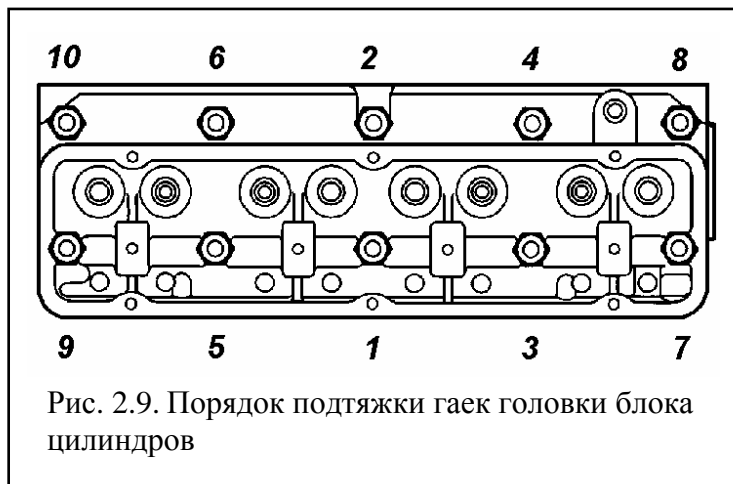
Порядок подтяжки гаек головки блока цилиндров
